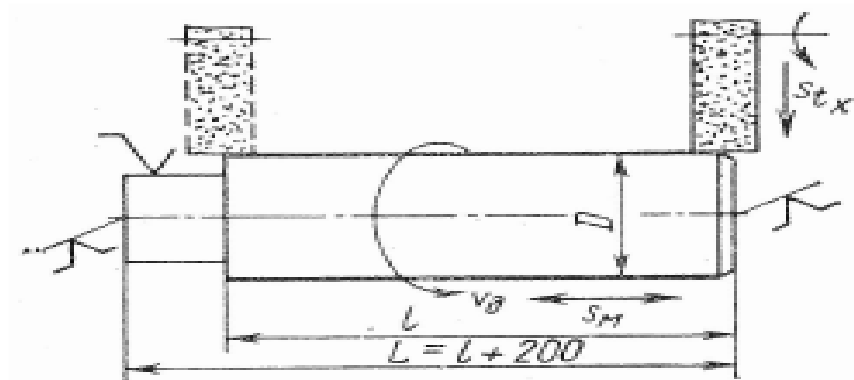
Ескіз круглого шліфування вала методом поздовжньої подачі.
